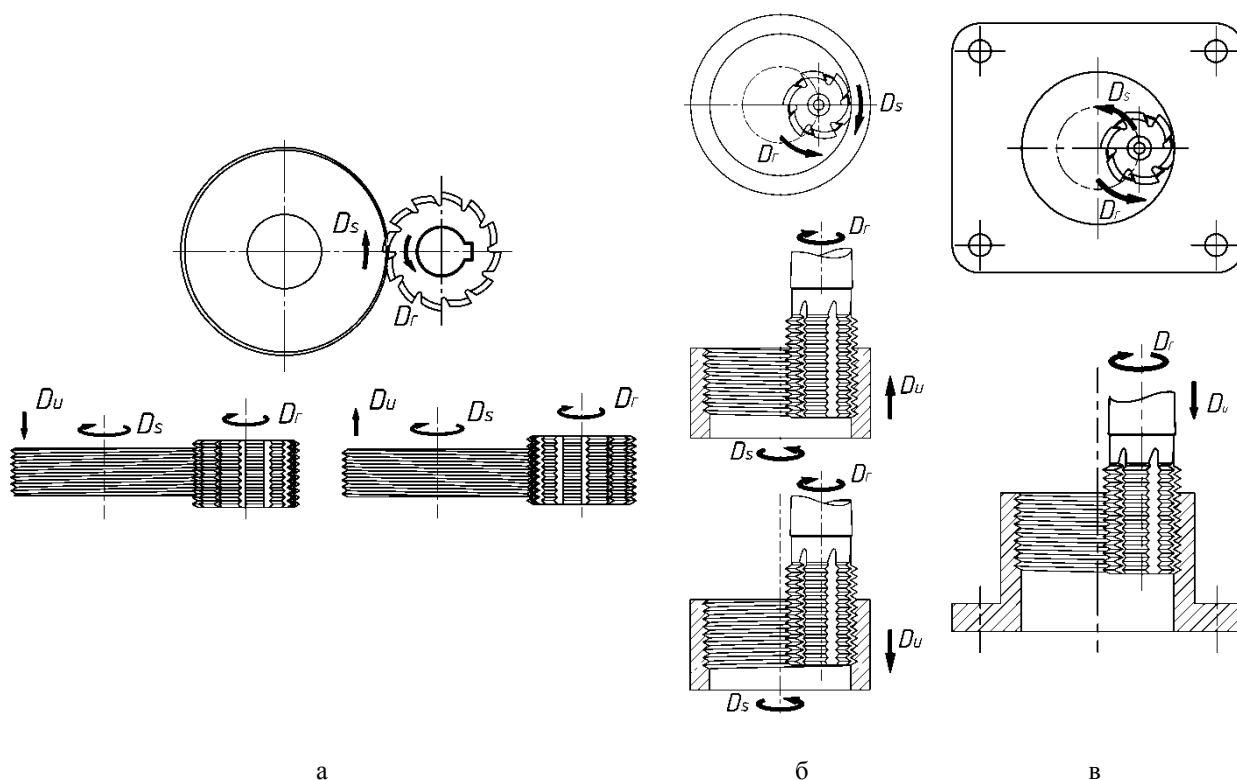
Фрезерование резьбы гребенчатой резьбовой фрезой: а - фрезерование правой и левой наружной резьбы, б – фрезерование правой и левой внутренней резьбы с использованием движения заготовки, в – фрезерование внутренней резьбы при неподвижной заготовке
